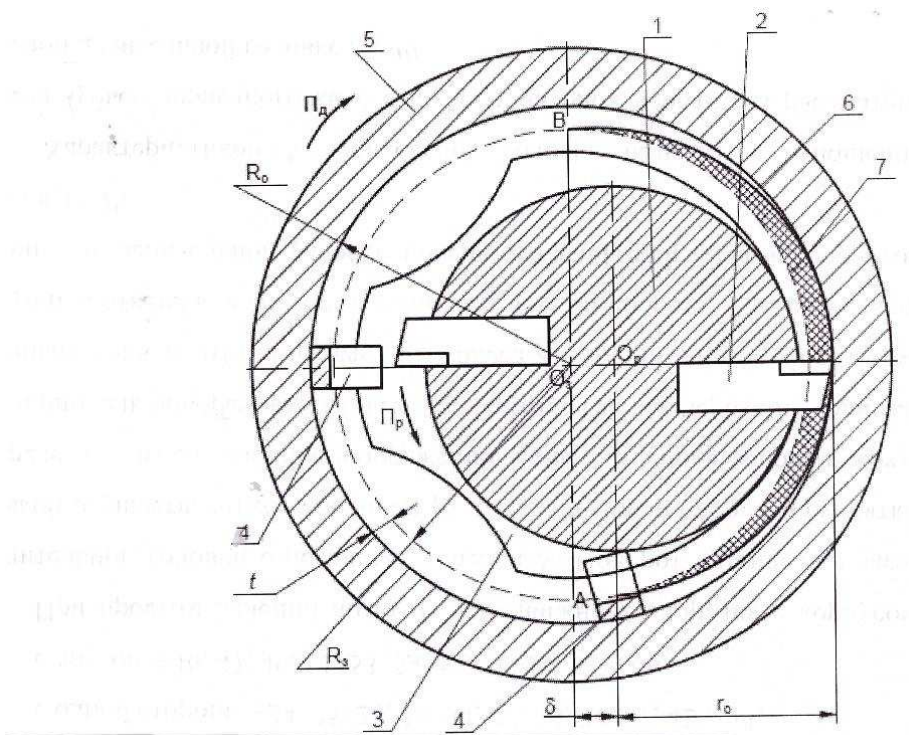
Схема вихревого растачивания отверстий. 1 – резцовая головка; 2- резец-вставка; 3 – борштанга; 4 – направляющая; 5- обрабатываемая деталь; 6 – сегмент срезаемой стружки; t- припуск на сторону в обрабатываемом отверстии; r_0 - радиус вращения резца – вставки 2; δ – смещение головки относительно оси отверстия; p_r – направление вращения резцовой головки; p_d – направление вращения детали
